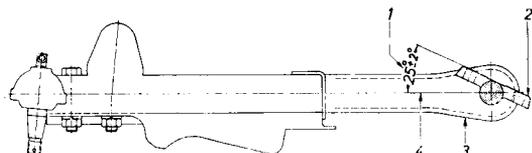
Winkel zwischen unterer Lenkerachse und Lenkerarmen
